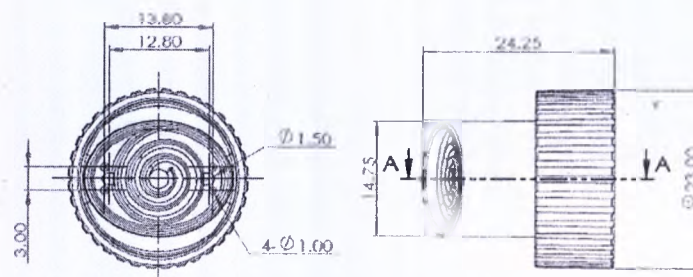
Схематичное изображение и габаритные размеры Полимерной одноразовой насадки Aqua большой
